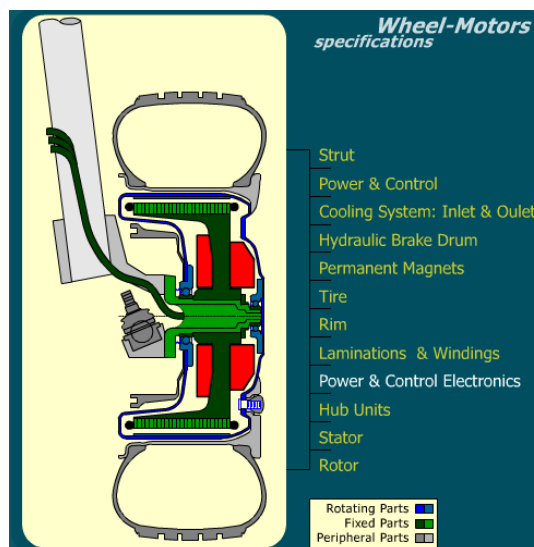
Desenho em corte da secção de um motor na roda com controlo integrado
